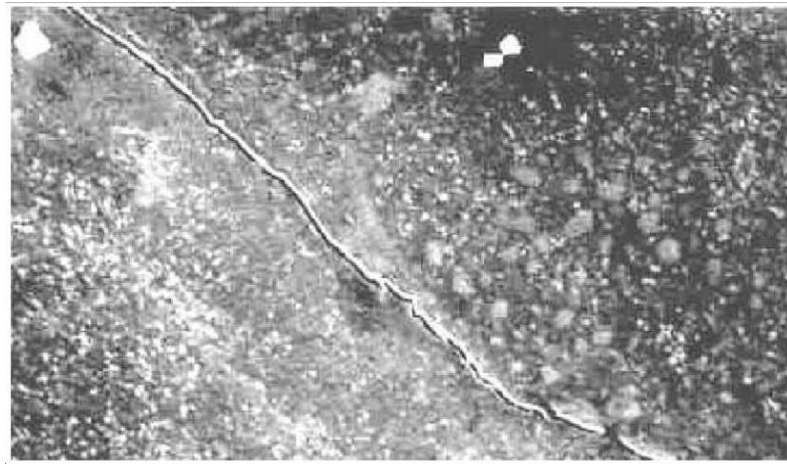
Corrosion Fatigue Cracking (CFC)
